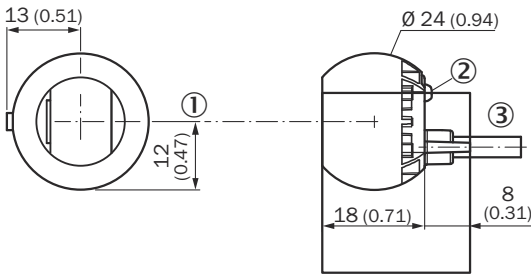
ZSE18-3xxxxx/ZT18-Cxxxxx
